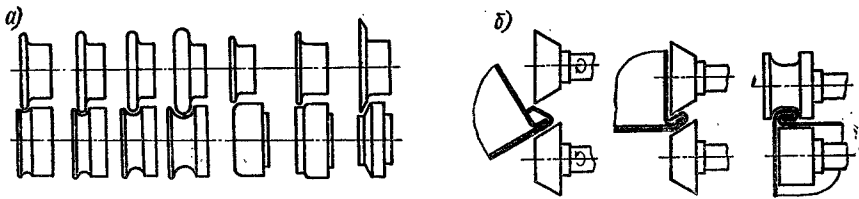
Комплект роликов для накатного станка (а) и закатка соединительных швов (б)
